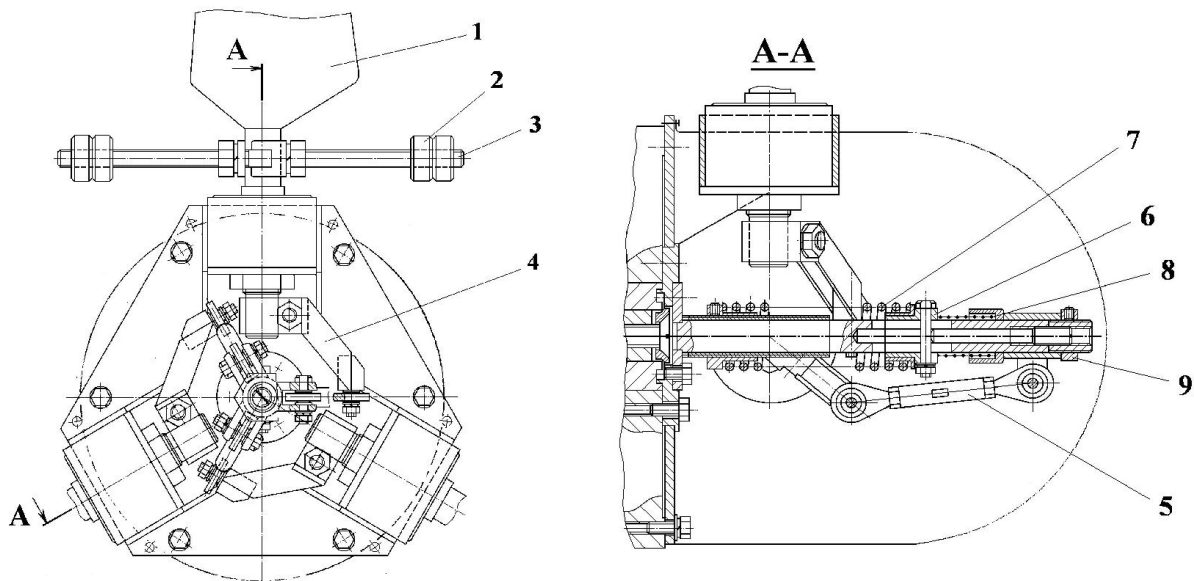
Загальна схема відцентрового регулятора ротора ВУ: 1 – лопать; 2 – відцентрові тягарці; 3 – державки відцентрових тягарців; 4 – кривошип; 5 – тяга; 6 – втулка; 7 – пружина регулювання; 8 – пружина пускова; 9 – упор.
